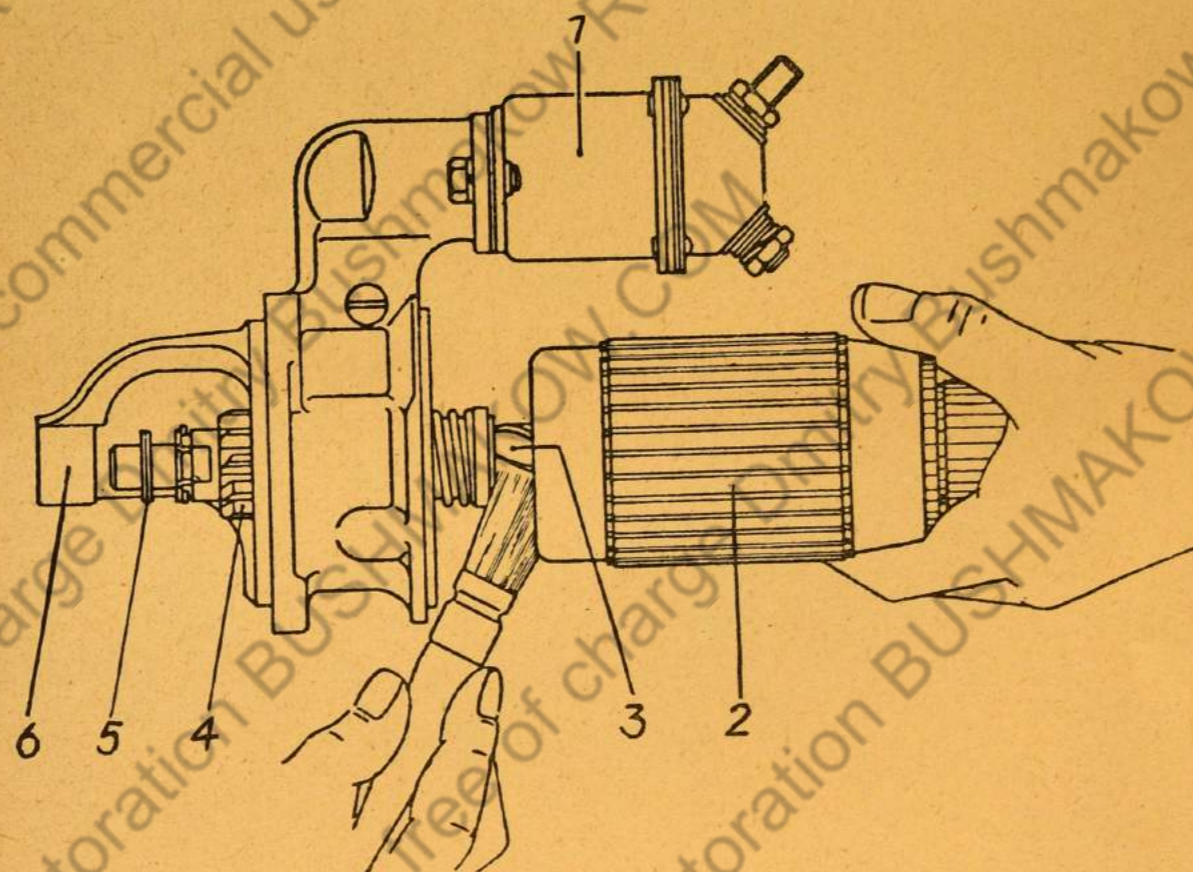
EGD-Anlasser, Abwaschen des Steilgewindes
